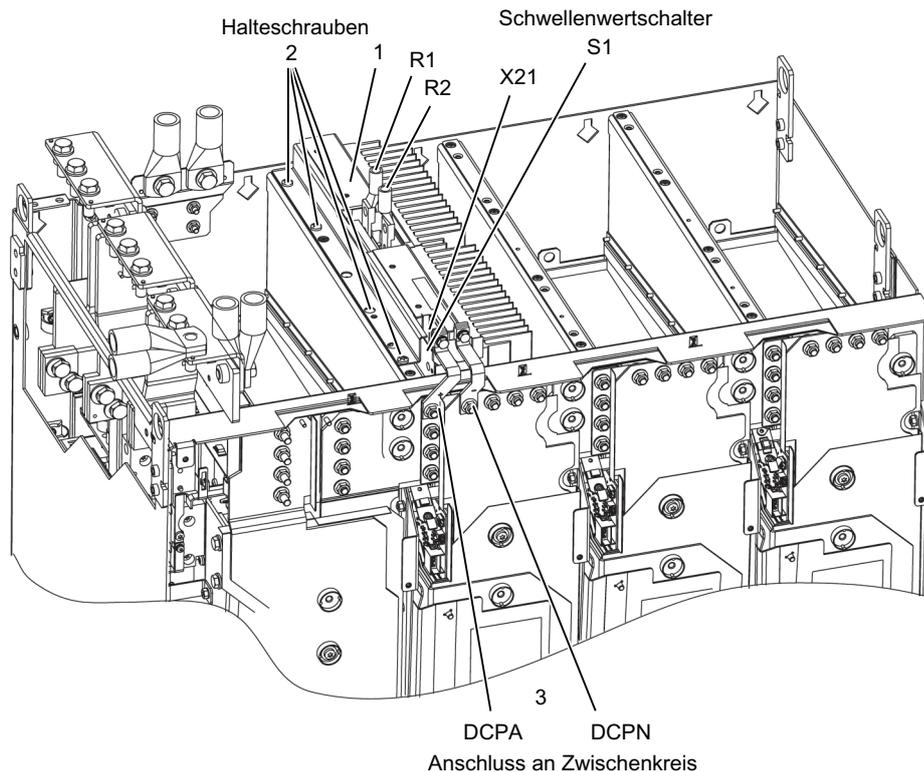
Montage des Braking Module in ein Power Module Bauform JX
